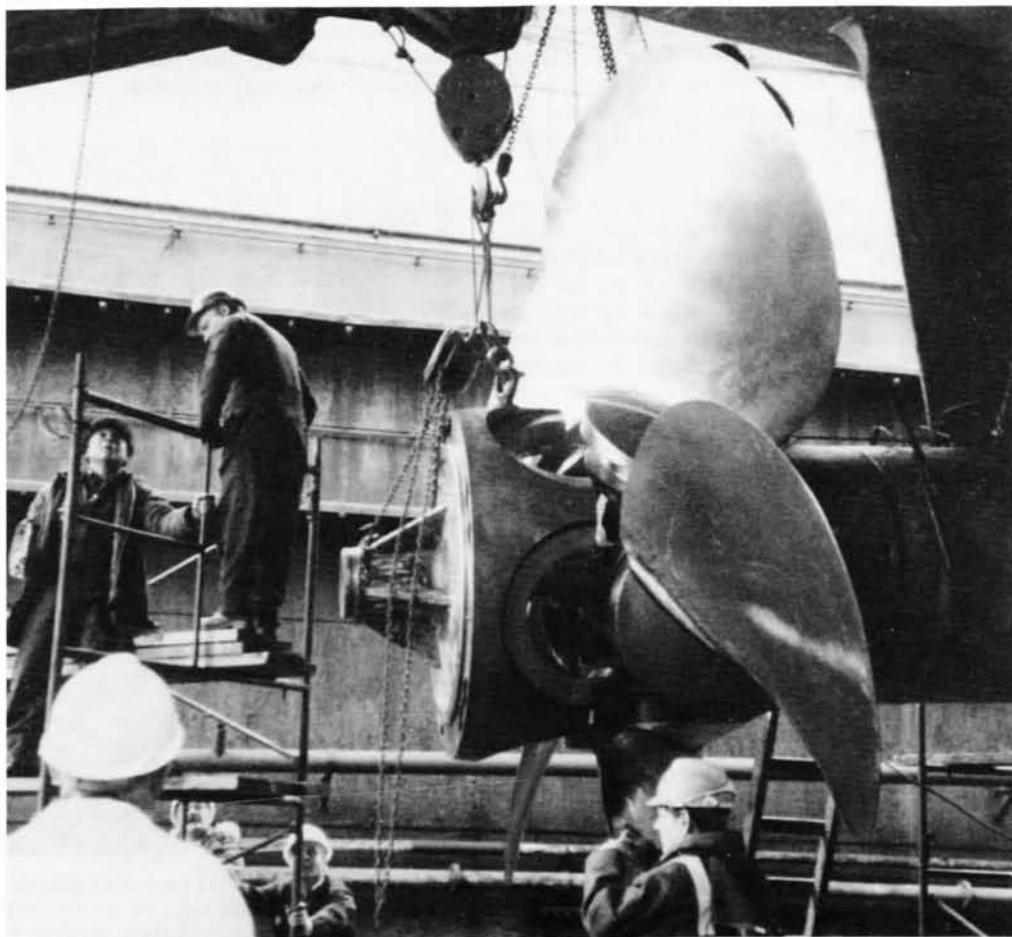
La section arrière du moyeu est déposée, découvrant la chape et les pieds des pales.
